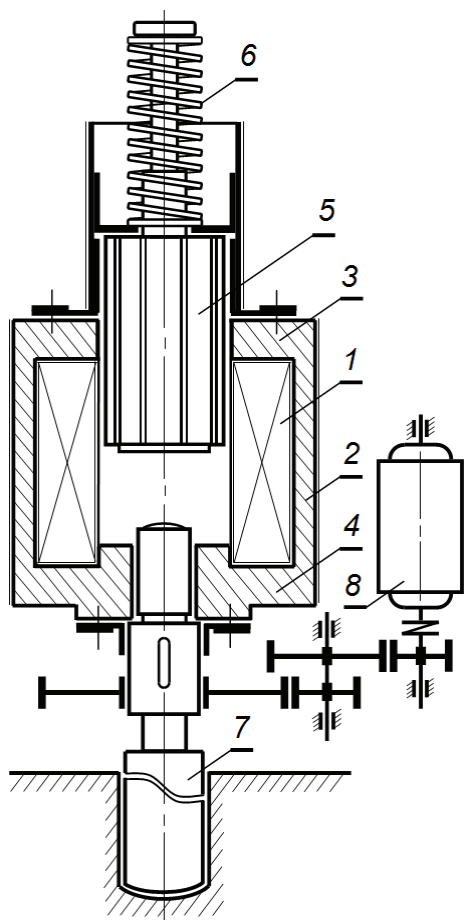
Схема конструкции ударного узла перфоратора: 1 – катушка возбуждения; 2 – ярмо магнитопровода; 3 – верхний полюс; 4 – нижний полюс; 5 – ударный боек; 6 – пружина сжатия; 7 – рабочий инструмент; 8 – двигатель механизма вращения рабочего инструмента
